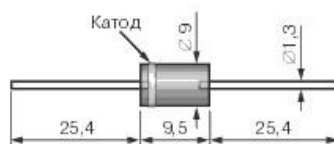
Габаритні розміри стабілітрон-1N5352BRLG
